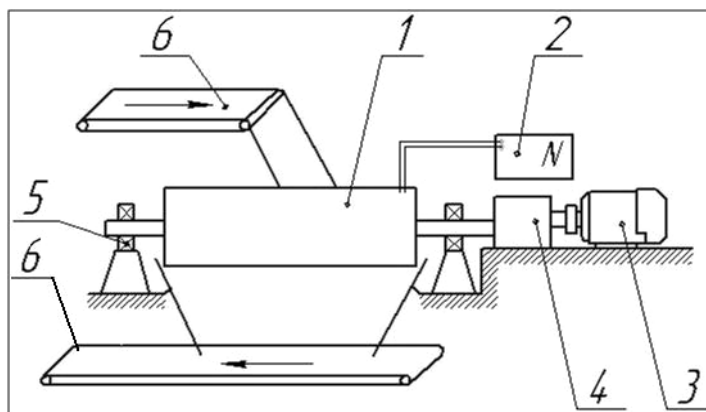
Основные конструктивные элементы установки для предпосевной обработки семян ИЭП
